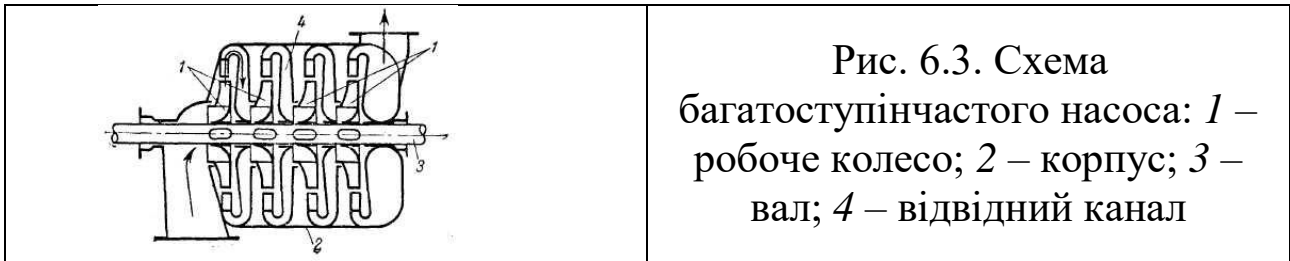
Схема багатоступінчастого насоса: 1 – робоче колесо; 2 – корпус; 3 – вал; 4 – відвідний канал
